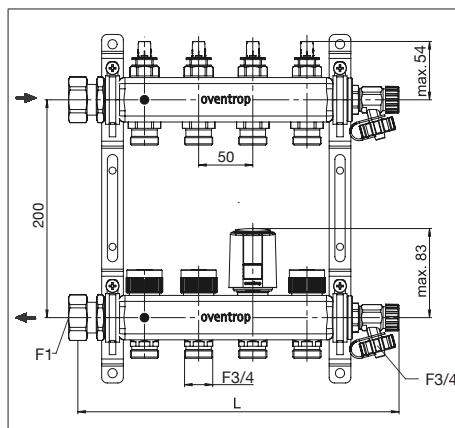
Dimensiuni distribuitor din inox „Multidis SFQ“, vedere frontală
